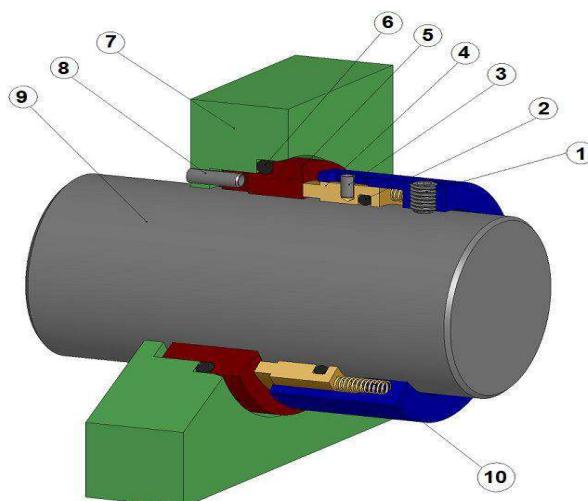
Многопружинное бессильфонное торцевое уплотнение: 1- монтажный болт для крепления уплотнения к валу насоса; 2- дополнительный уплотнитель; 3- штифт передающий крутящий момент вращающемуся кольцу; 4- подвижное кольцо; 5- стационарное кольцо; 6- уплотнительный материал из эластомера; 7- корпус насоса; 8- стопорный штифт стационарного кольца; 9- вал насоса; 10- поджимная пружина.
